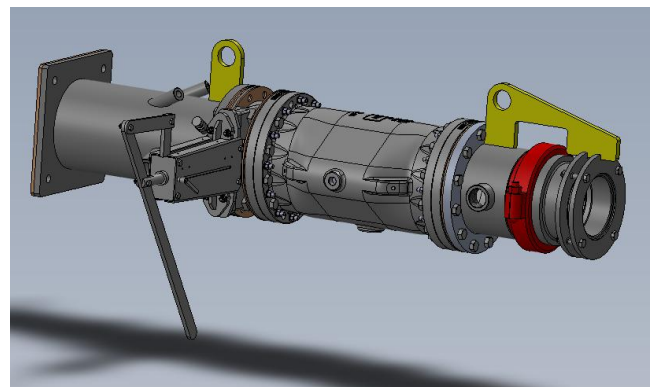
SAS Hi'Drill® équipée d'un double dispositif d'étanchéité
